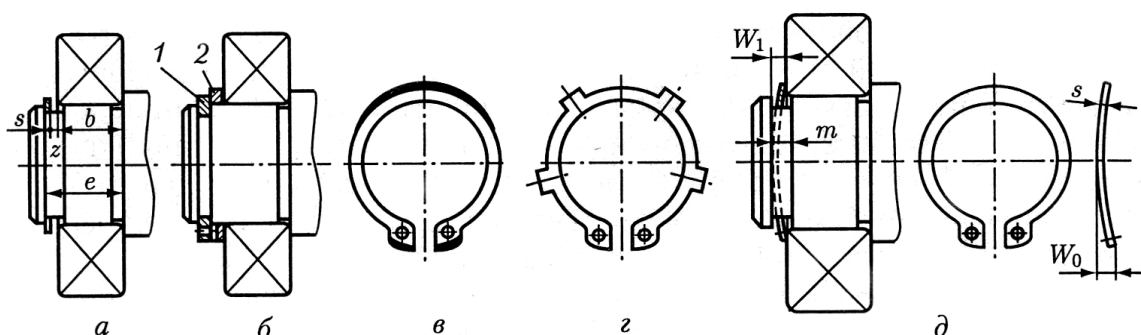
Крепление подшипников на валах пружинным упорным плоским кольцом:
